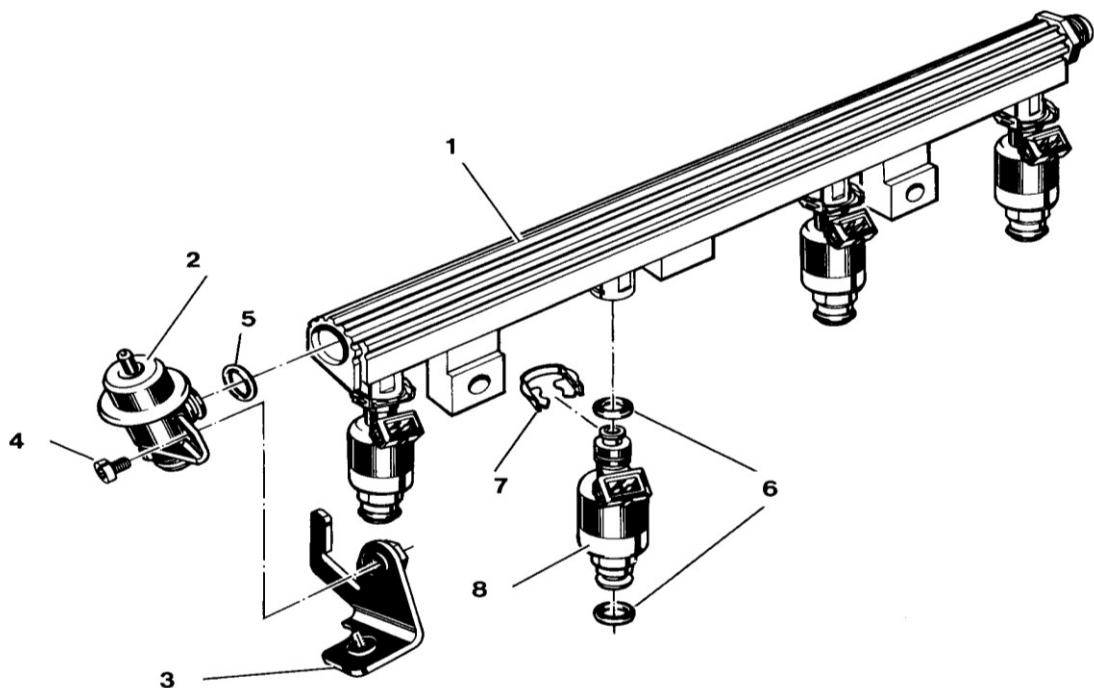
Топливная рампа системы РВТ в сборе с форсунками и стабилизатором давления топлива: 1- рампа; 2 –регулятор давления топлива; 3 – кронштейн; 4 – болт; 5, 6 – резиновые уплотнительные кольца; 7 – фиксатор форсунки; 8 - форсунка
